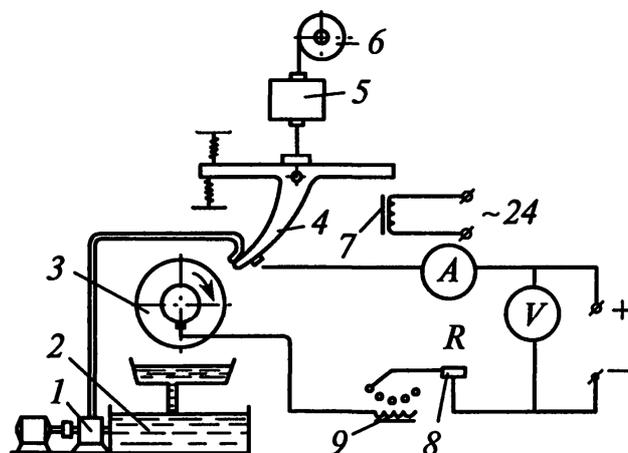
Схема установки для вибродуговой наплавки: 1 – насос; 2 – бак; 3 – деталь; 4 – мундштук; 5 – механизм подачи; 6 – кассета; 7 – вибратор; 8 – реостат; 9 – дроссель
